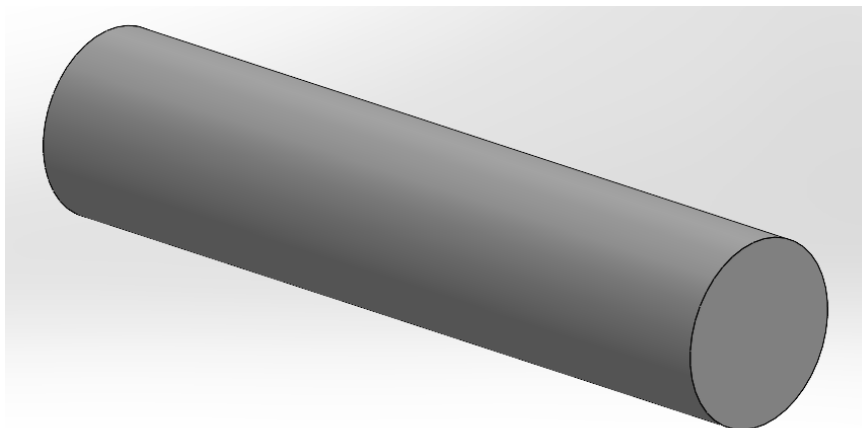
Тривимірна модель заготовка гвинта
